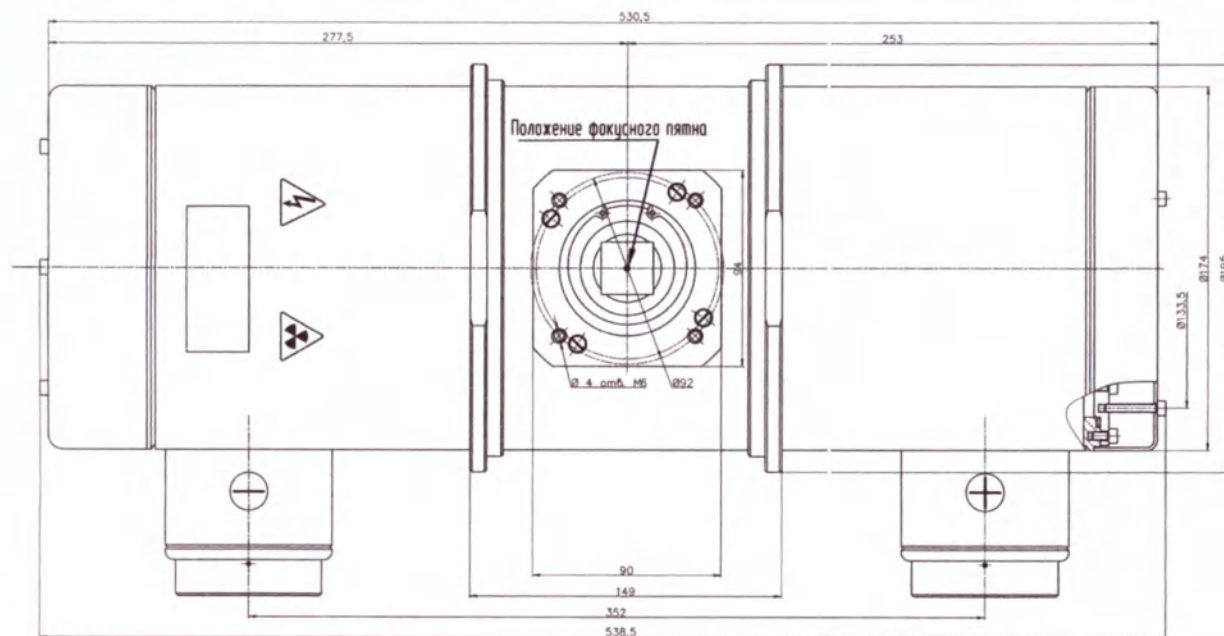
Присоединительные размеры и положение фокусного пятна излучателя (кожуха с рентгеновской трубкой).
